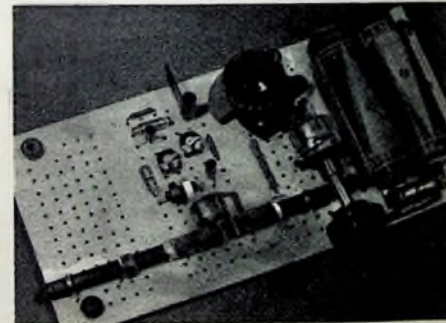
Ansicht des gesamten Chassis mit Einzelteilen
